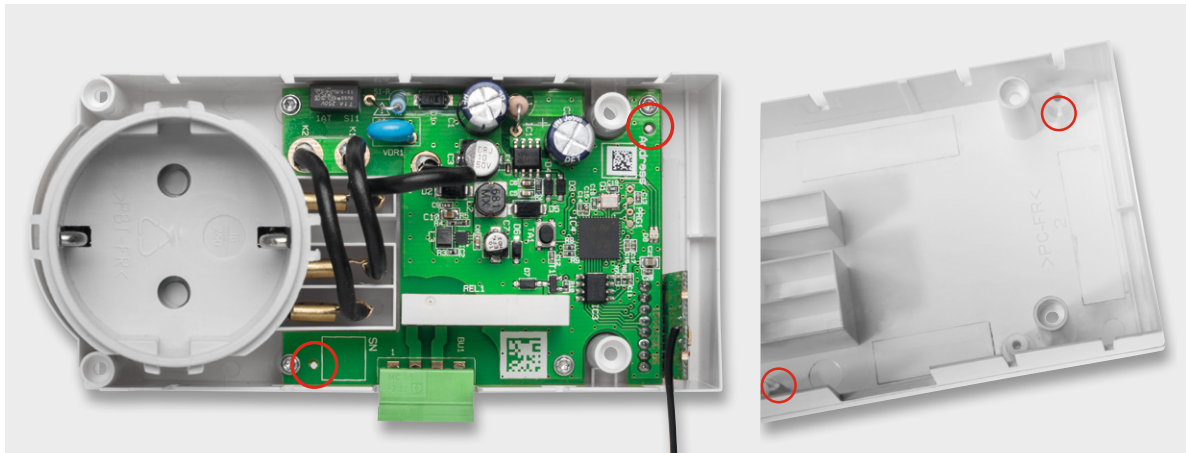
Beim Einlegen der Platine in das Gehäuse ist auf den richtigen Sitz der Fixiernasen des Gehäuses in der Platine zu achten.
